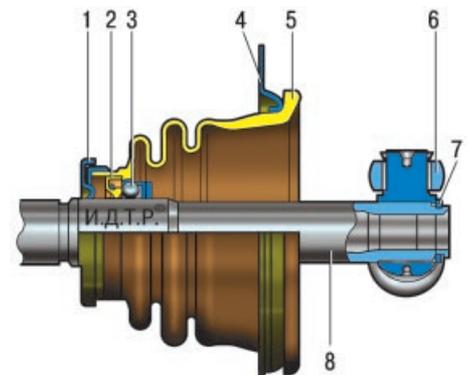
Левый внутренний шарнир равных угловых скоростей: 1 – грязеотражатель; 2 – сальник; 3 – подшипник; 4 – держатель чехла; 5 – чехол шарнира; 6 – ролик трехшиповой ступицы; 7 – стопорное кольцо; 8 – вал привода
